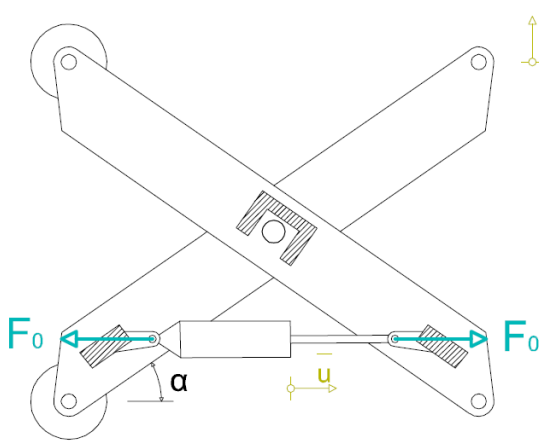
Mecanismo con el cilindro en posición horizontal
